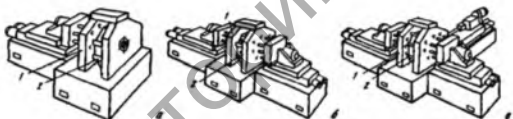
Типовые компоновки агрегатных станков с поворотным делительным барабаном
